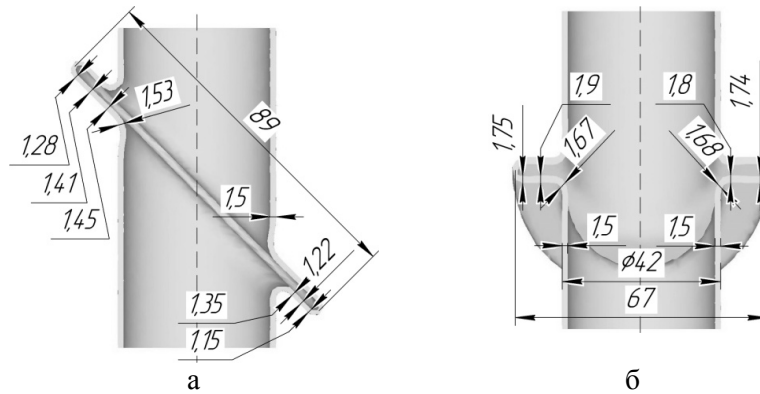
Форма та розміри здеформованої заготовки: а – в розрізі по найбільшому розміру фланця, б – в розрізі по найменшому розміру фланця
